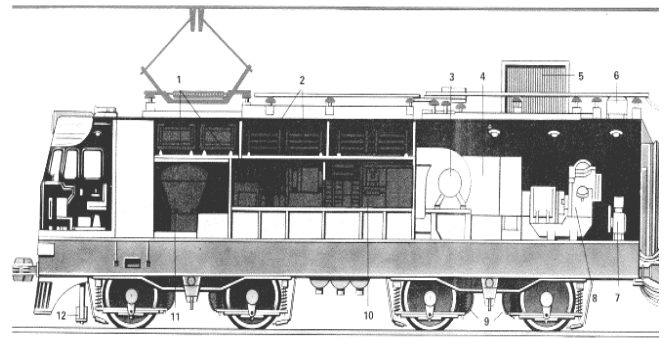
Локомотивний лубрикатор на базі електровоза ВЛ-11м
